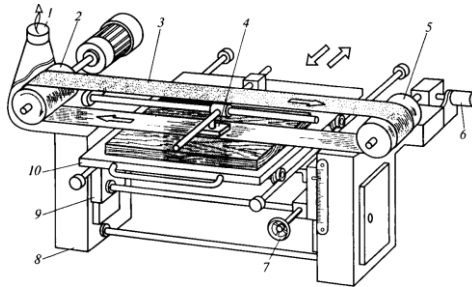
Стрічковий шліфувальний верстат з рухомим столом: 1 – огороження-пилеприймач; 2 – приводний шків; 3 – шліфувальна стрічка; 4 – утюжок; 5 – не приводний шків; 6 – пневмоциліндр; 7 – маховичок; 8 – тумба; 9 – супорт; 10 – стіл
